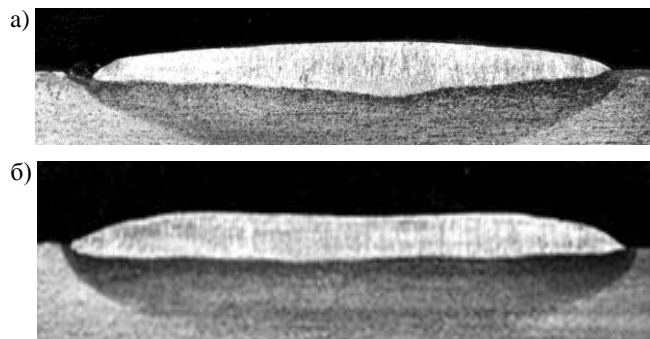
Форма валика и характер проплавления при наплавке двумя лентами Св-08Х25Н13 сечением 60×0,5 мм: а) – $N = 0,50$; б) – $N = 0,60$
